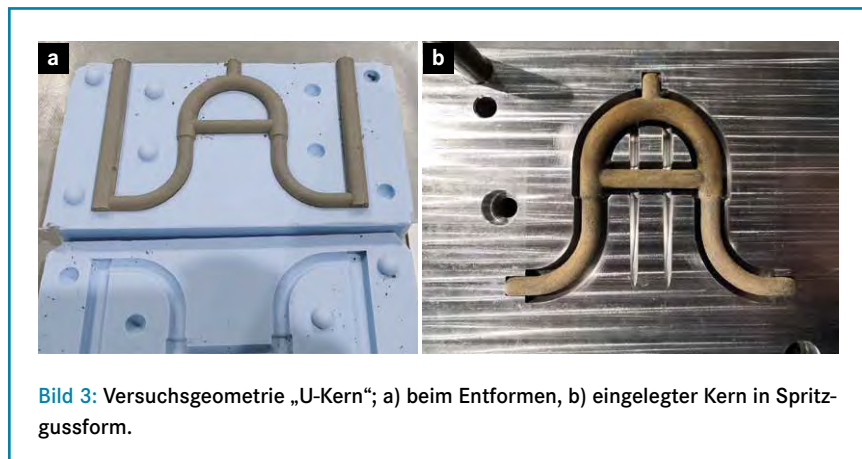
Versuchsgeometrie „U-Kern“; a) beim Entformen, b) eingelegter Kern in Spritzgussform.
